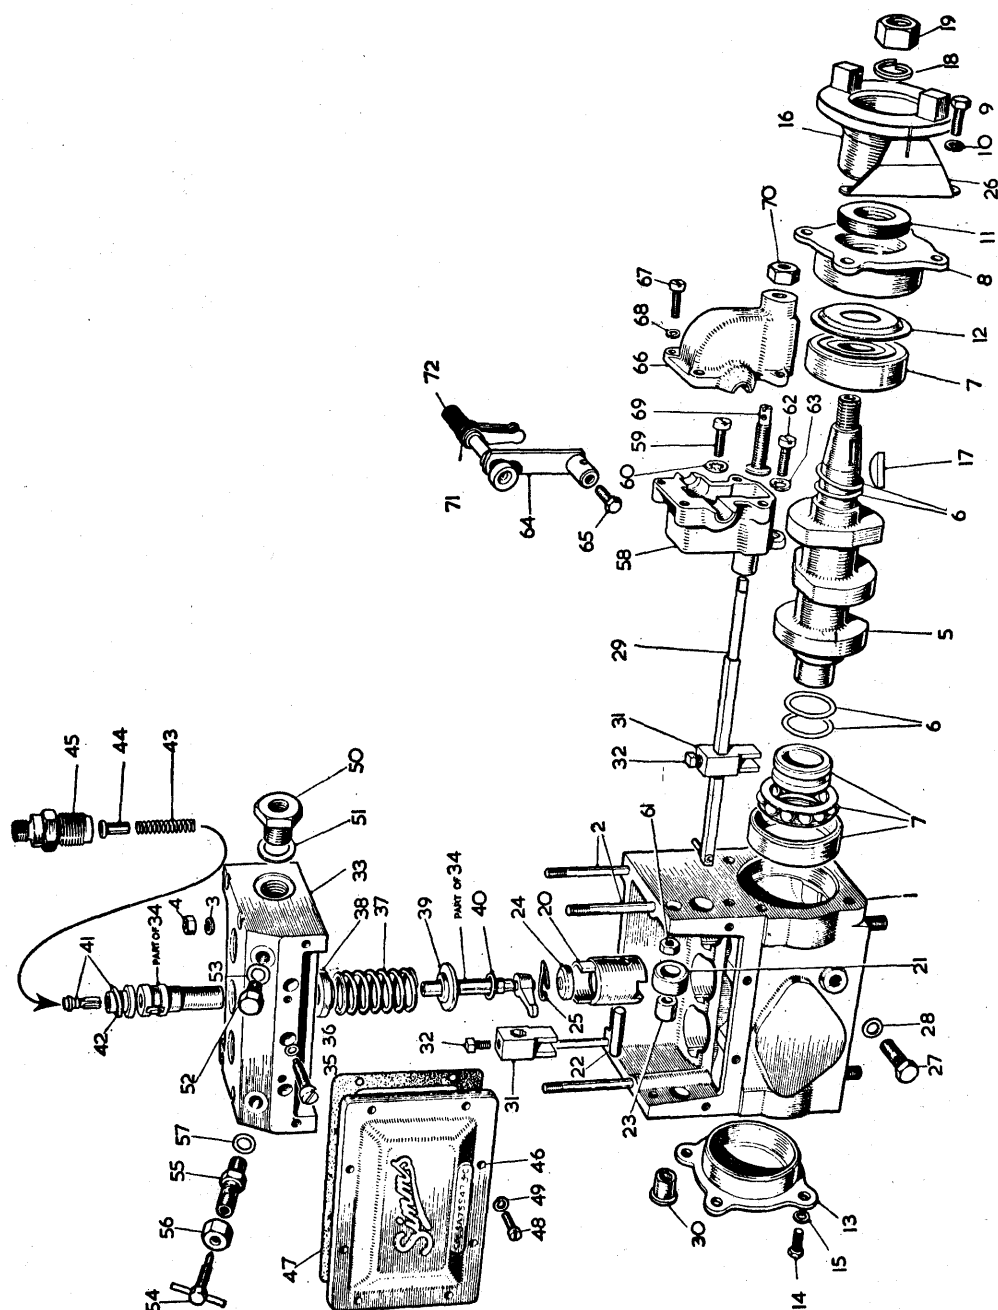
Exploded-view af SIMMS indsprøjtningpumpe.
